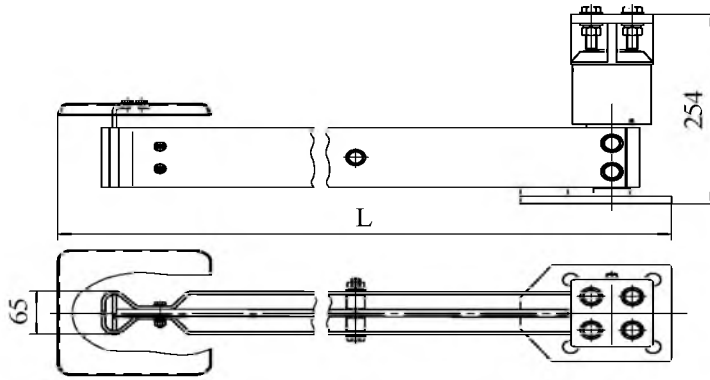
Нож контактный для РН(П)(С)К СЭЩ-110/2000
